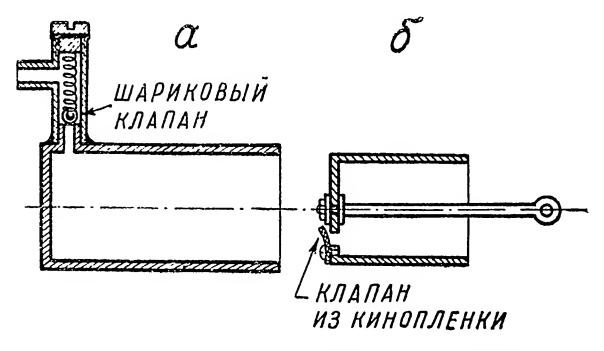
Клапаны компрессора: а — шаровой в цилиндре; б — из кинопленки в поршне
